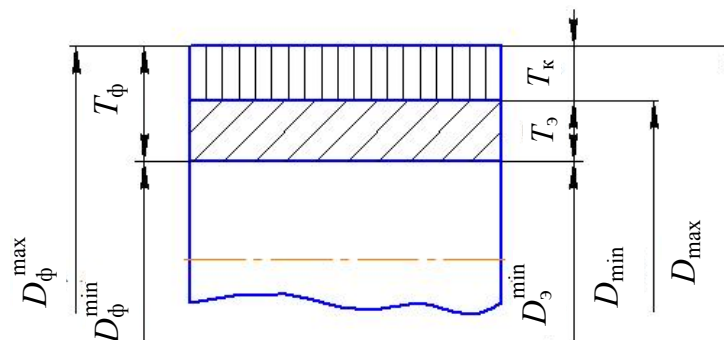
Схема расположения полей допусков охватываемой детали
